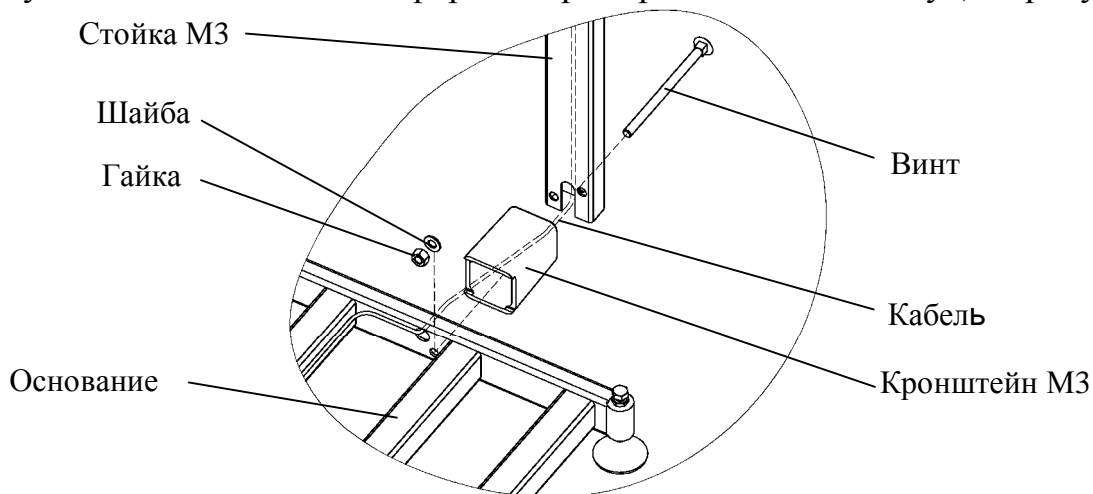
Крепление прямоугольной стойки к основанию весовой платформы ТВ-М\_A
